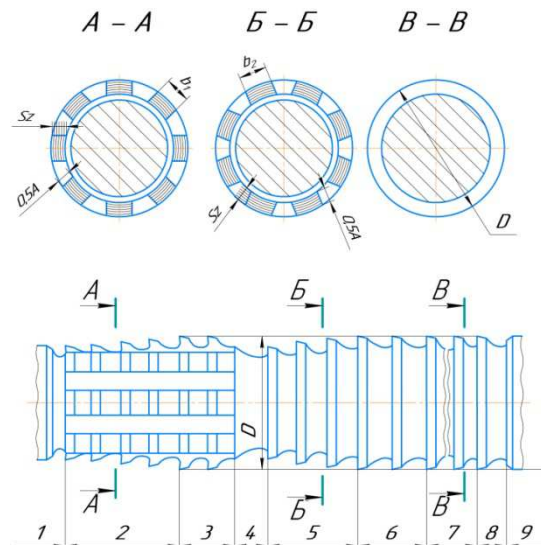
Двухступенчатая прогрессивная протяжка для обработки цилиндрических отверстий
